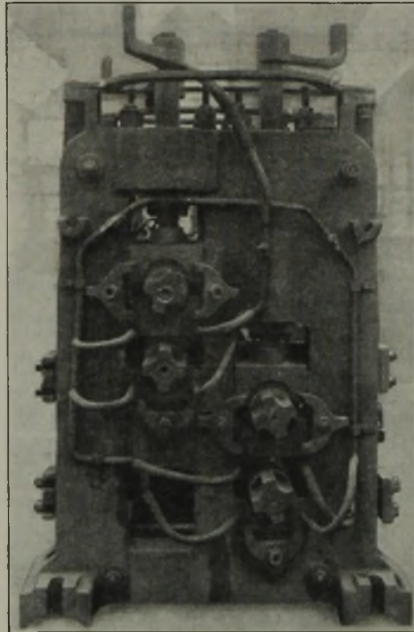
Kühlwasserleitungen und Einbau am 250er Doppel-Duo-Gerüst.
